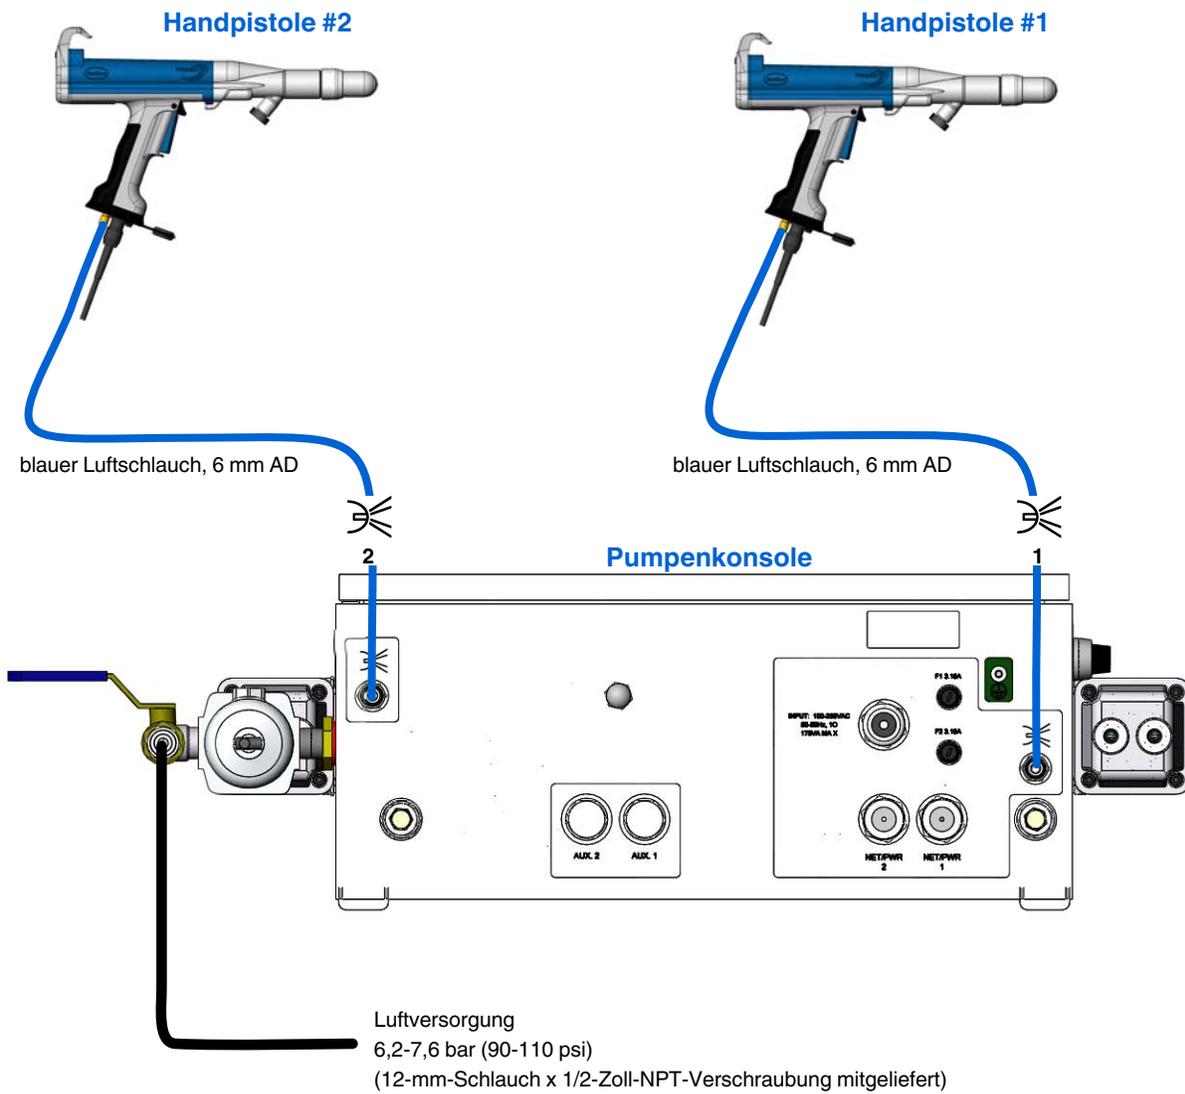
Systemluftversorgung und Pistolenluftanschlüsse
